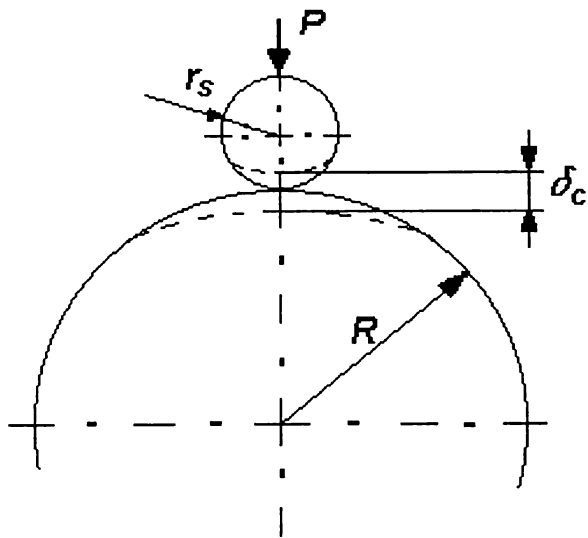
Schemă explicativă pentru contactul exterior palpator sferic-piesă cilindrică
